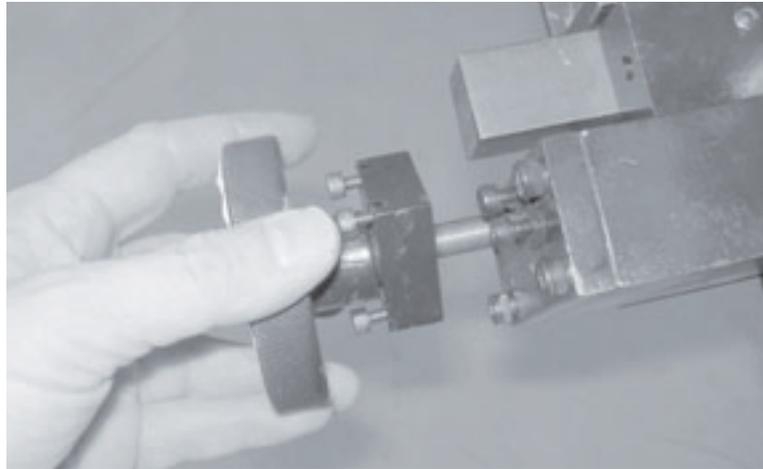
Ziehen Sie den Werkzeughalter zurück, damit das Werkzeug nicht in Kontakt mit der Rohrseite kommt, während Sie den Werkzeugschlitten einstellen.
